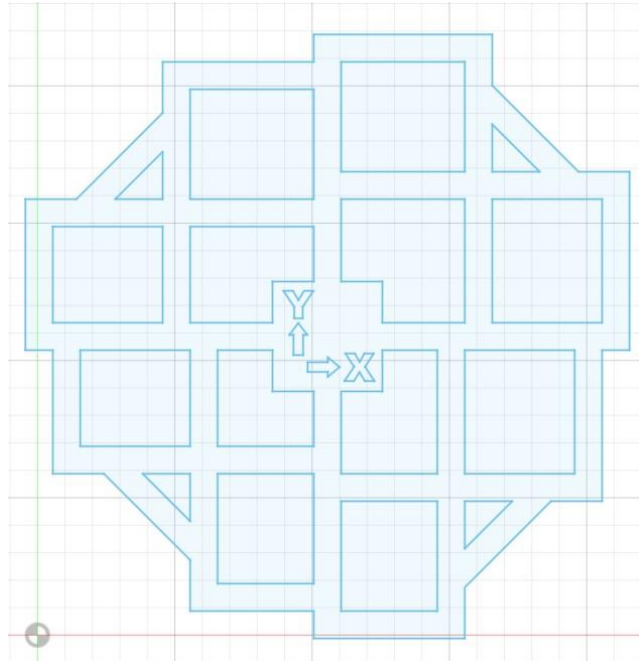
Diseño de la pieza del ensayo en Fusion 360. (Elaboración propia)
